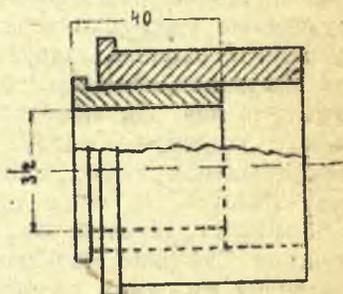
Сборная втулка для крепления заготовки и обточки до  $\varnothing 26,6$  мм по длине 1800 мм
